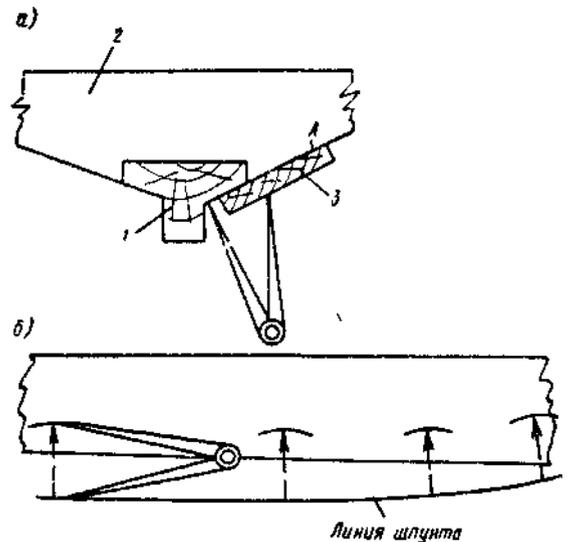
Причерчивание шпунтового пояса обшивки: а — поперечное сечение; б — боковой вид.
